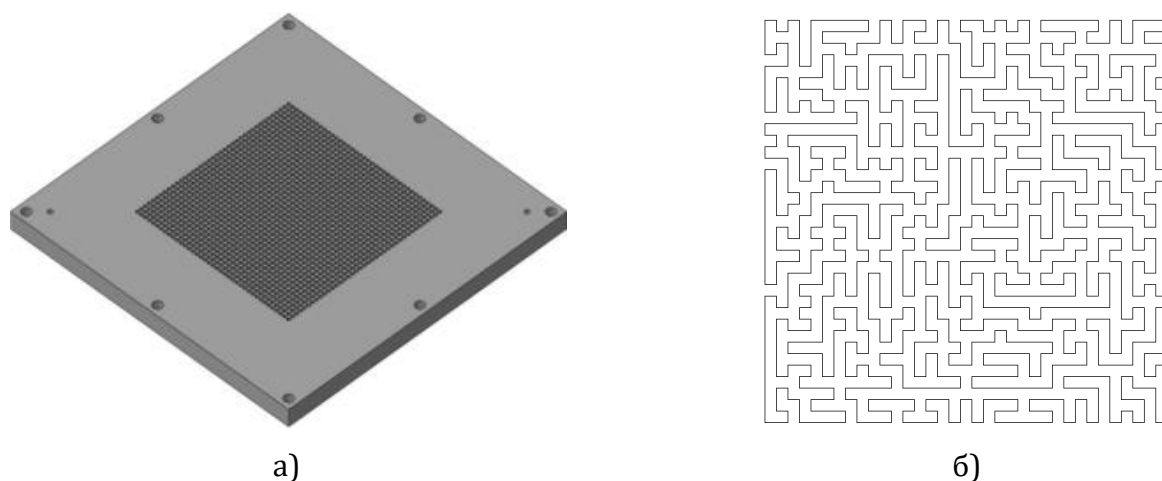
3D-модель матрицы (а) и путь сверла (б) при её изготовлении
